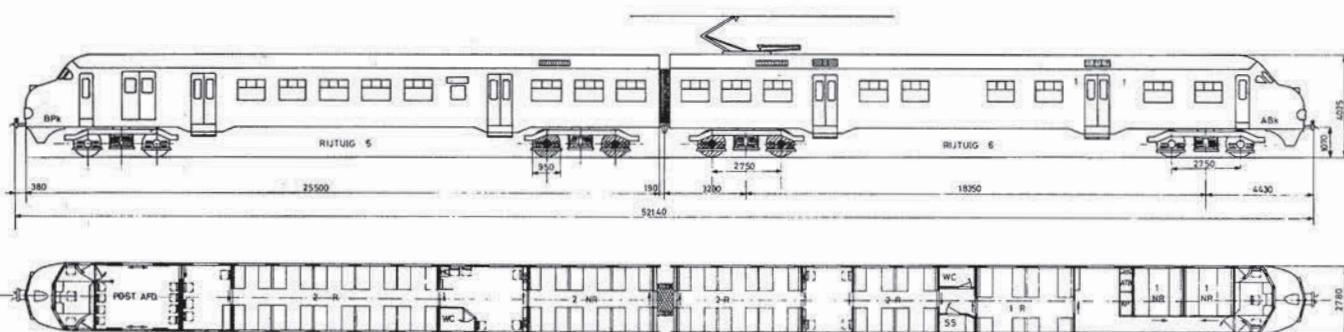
Algemeen plan treinstellen 801 - 840, levering Werkspoor
